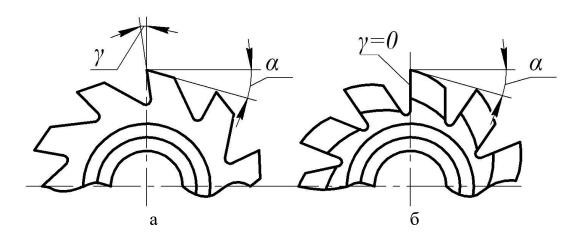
Фома зубьев фрез: а – острозаточенных, б – затылованных
